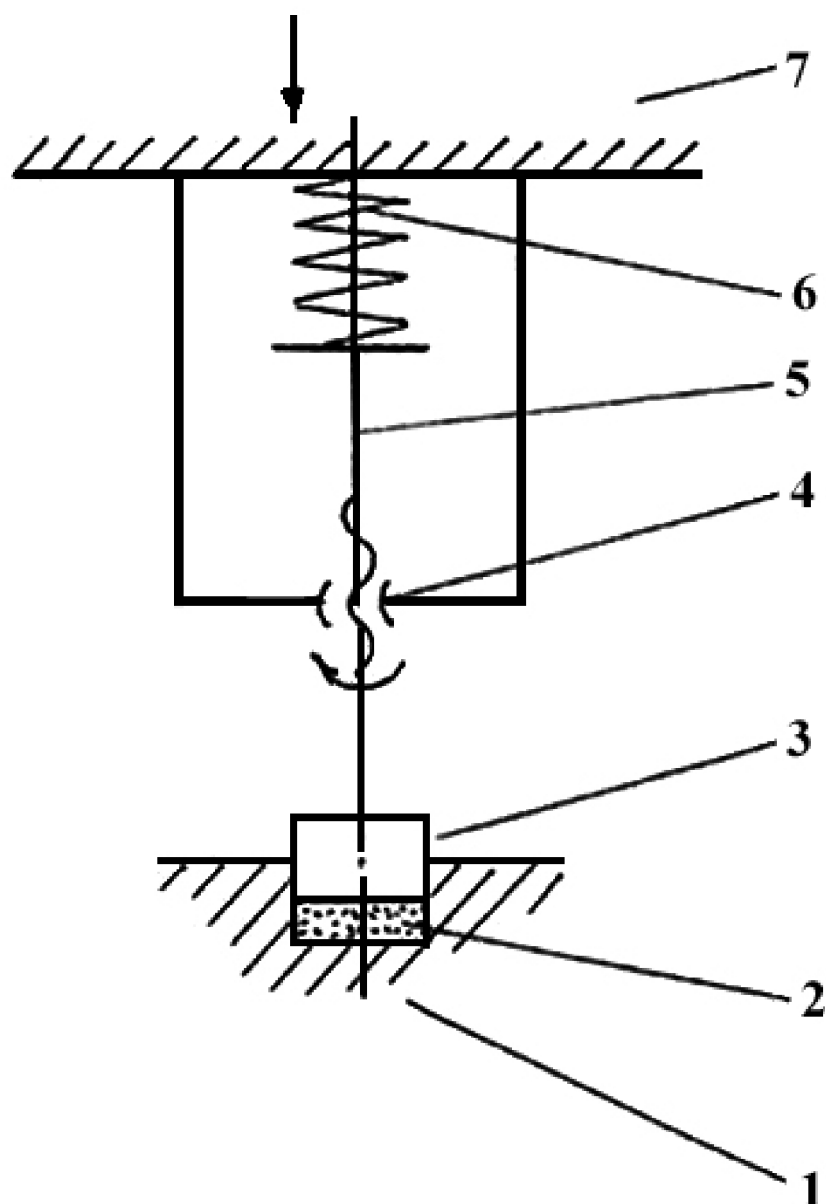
Схема штампа для формования порошковой детали со сдвигом частиц
